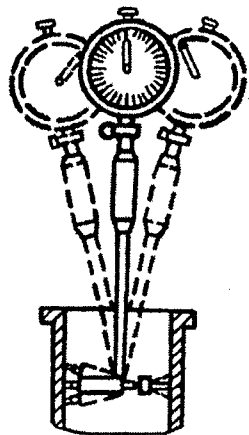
Измерение диаметра зеркала цилиндра индикаторным нутромером.
